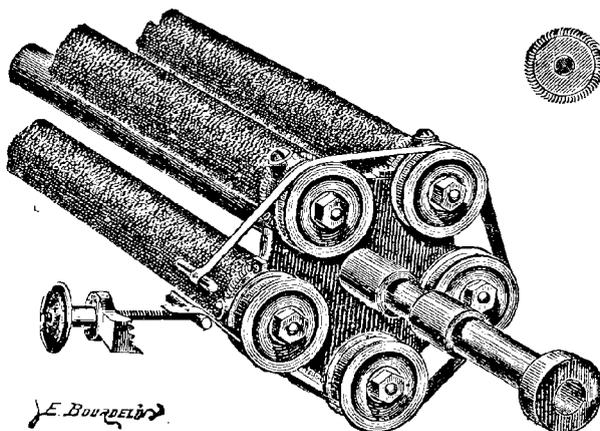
Tambour laineur de la machine Gosselin; extrémité portant la courroie de commande. Coupe d'un travailleur.
